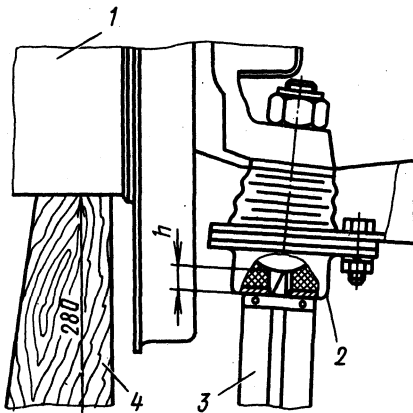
Проверка нижнего шарового шарнира передней подвески автомобиля «Жигули»:
